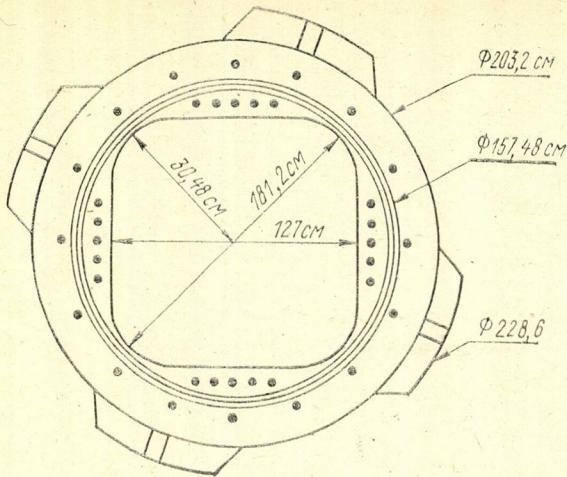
Стандартный стыковочный узел американской орбитальной станции
